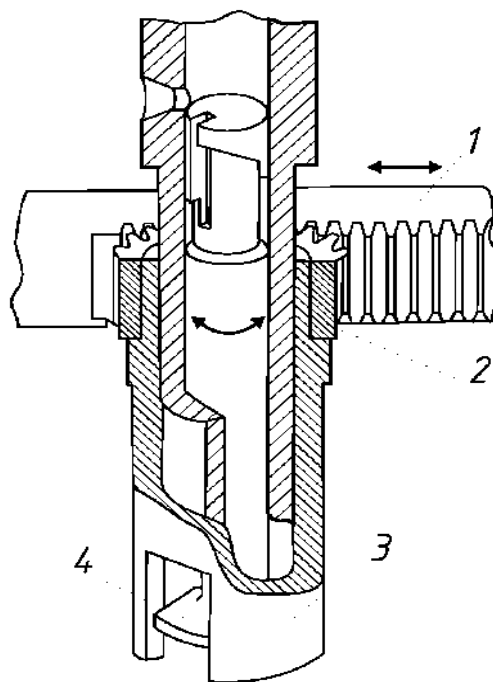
Зубчато-рейкова передача для провертання плунжера:
